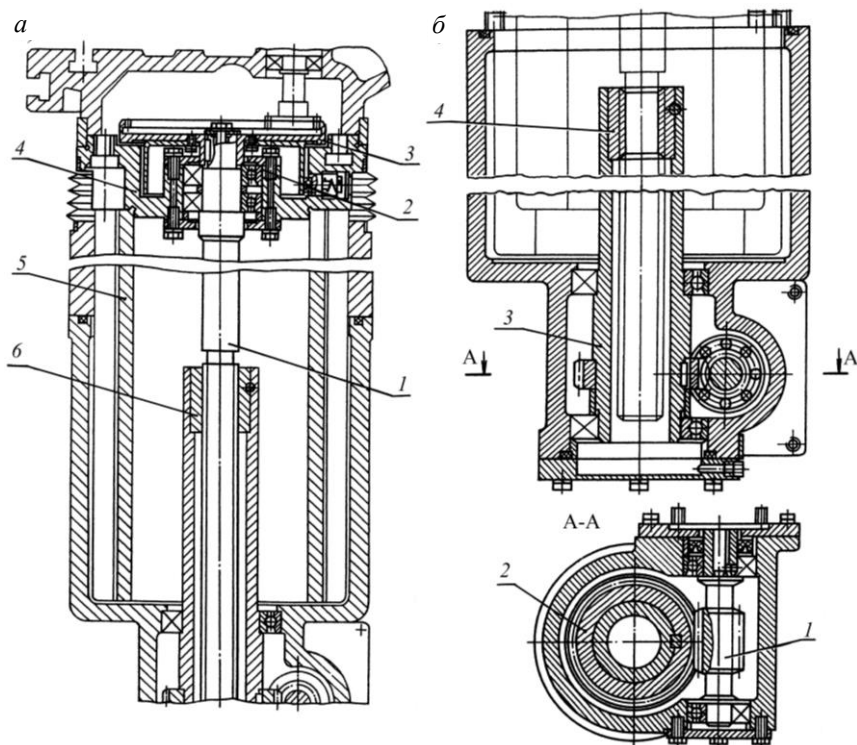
Механизм и редуктор подъема шлифовальной бабки универсально-заточного станка модели ЗД642Е
